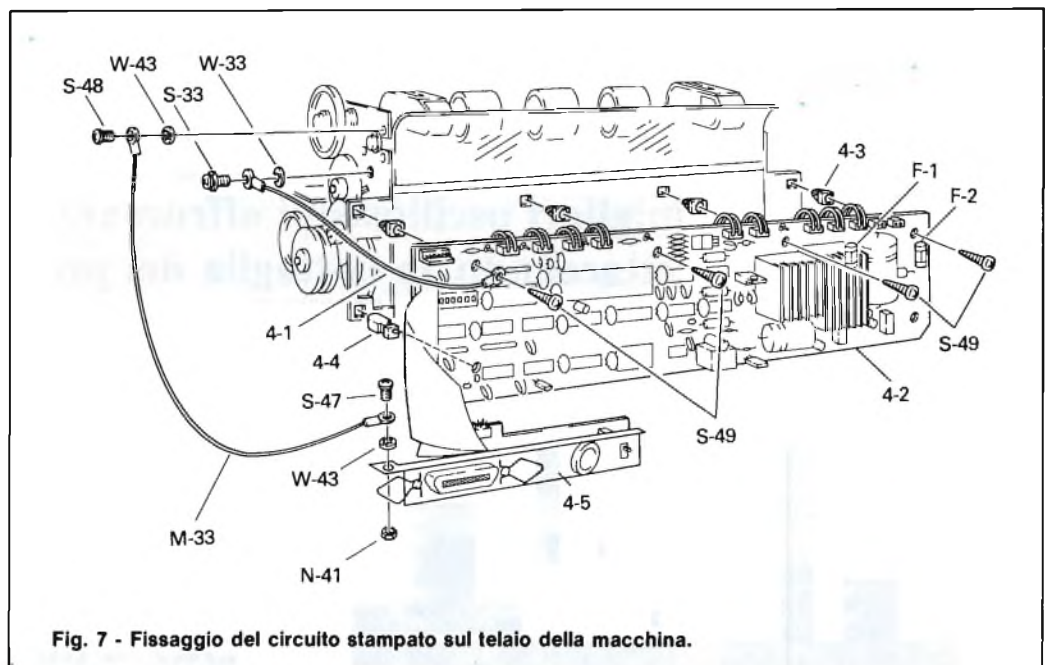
Fissaggio del circuito stampato sul telaio della macchina.
